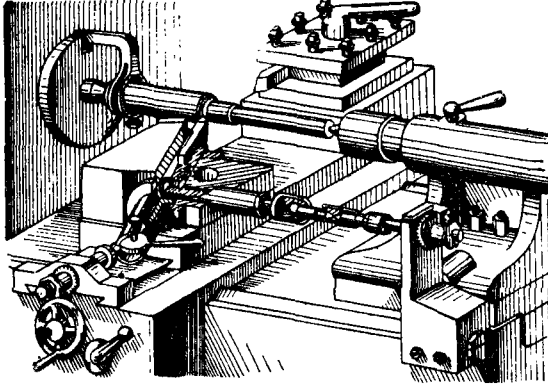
Установка копировального приспособления (по рис. 48) и резцедержателя при obtачивании ступенчатых валков.
